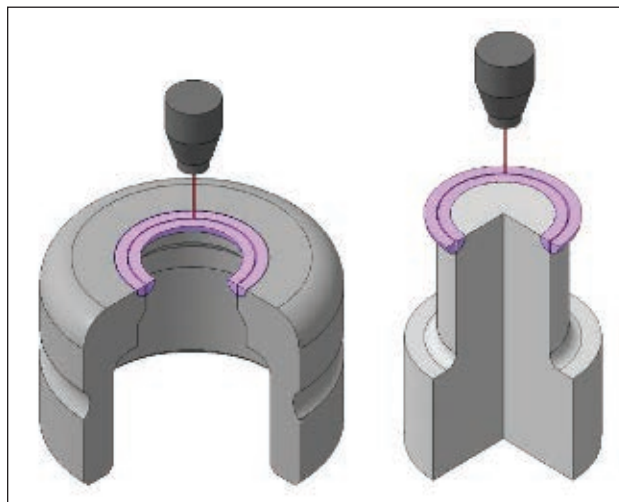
Газолазерная резка по боковой поверхности матрицы и пуансона
